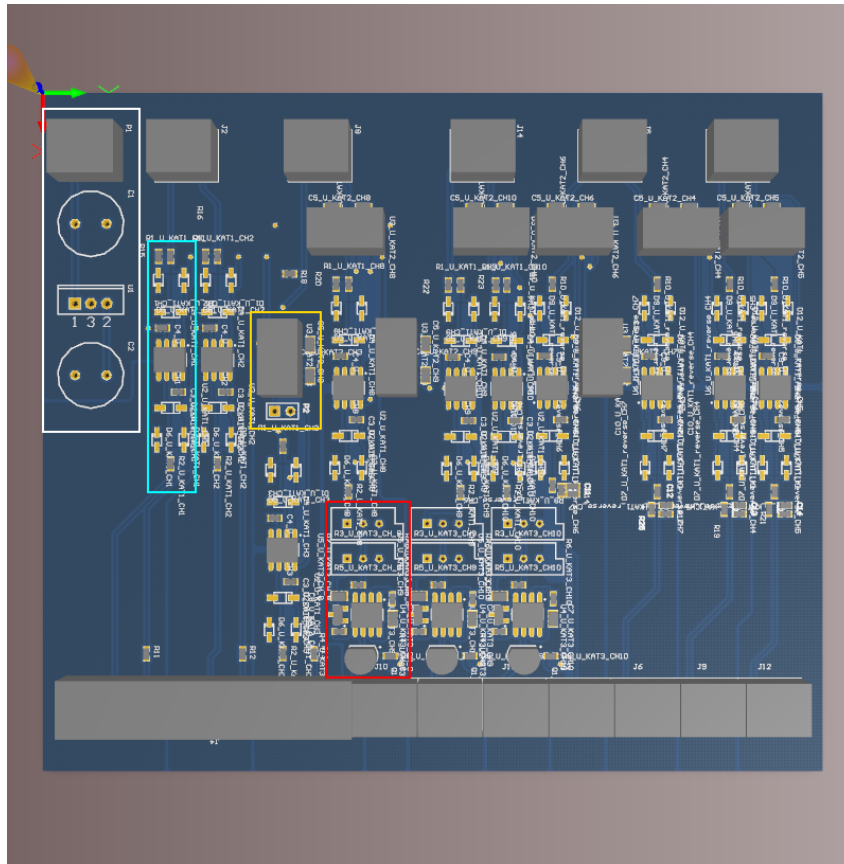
3D-Modell des PCB Emulation Board
